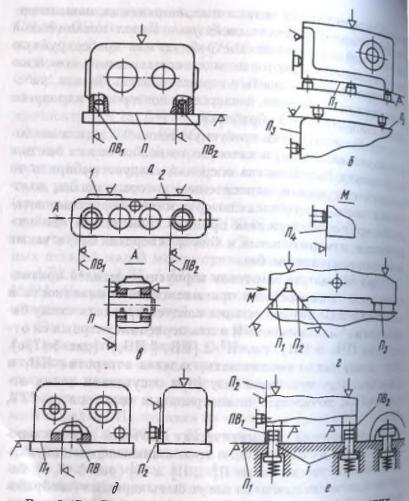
Схемы базирования заготовок призматических корпусных деталей
